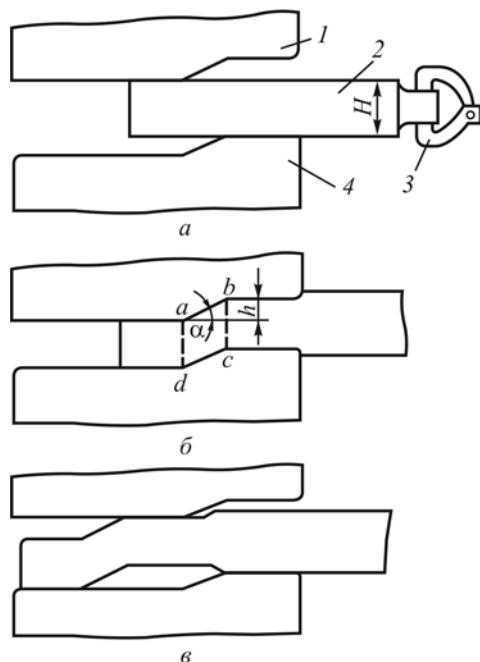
Схема ковки в бойках со ступенчатой рабочей поверхностью:
